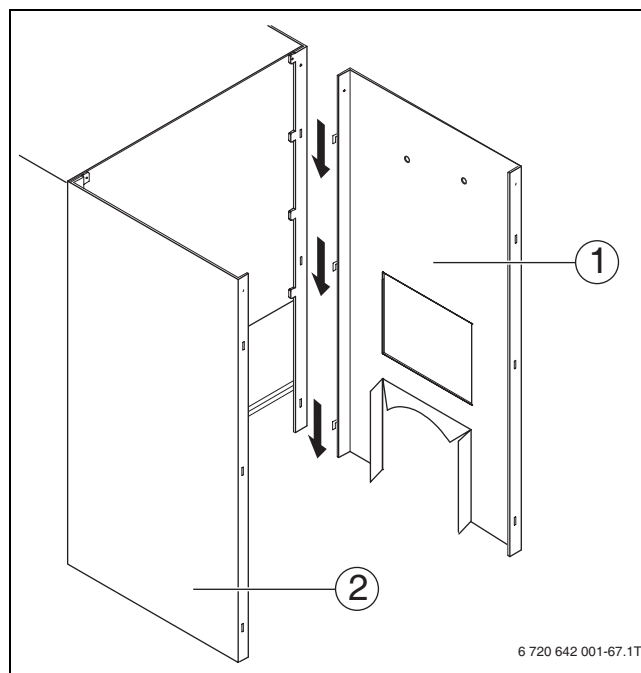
SP161-9: Přehnutí jazýčků přední stěny
